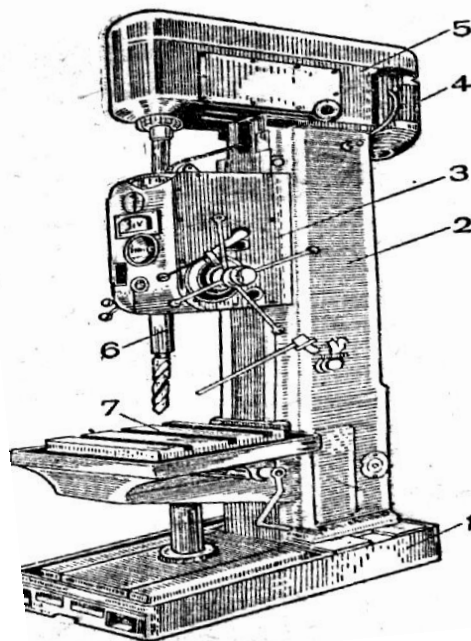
Загальний вид свердлильного верстата (модель 2А 150)
